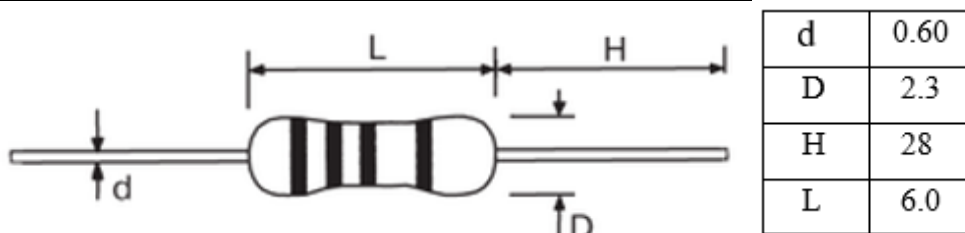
Розміри постійного резистора в корпусі MFR5
